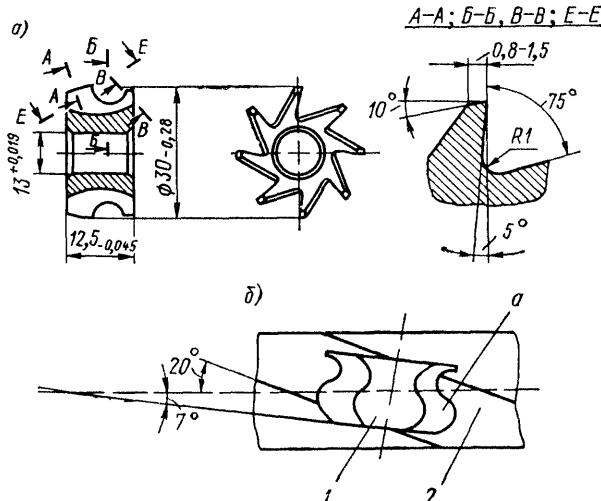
Фреза для одновременной обработки канавки и спинки на заготовках шпоночных фрез (а) и схема установки ее относительно заготовки (б)
